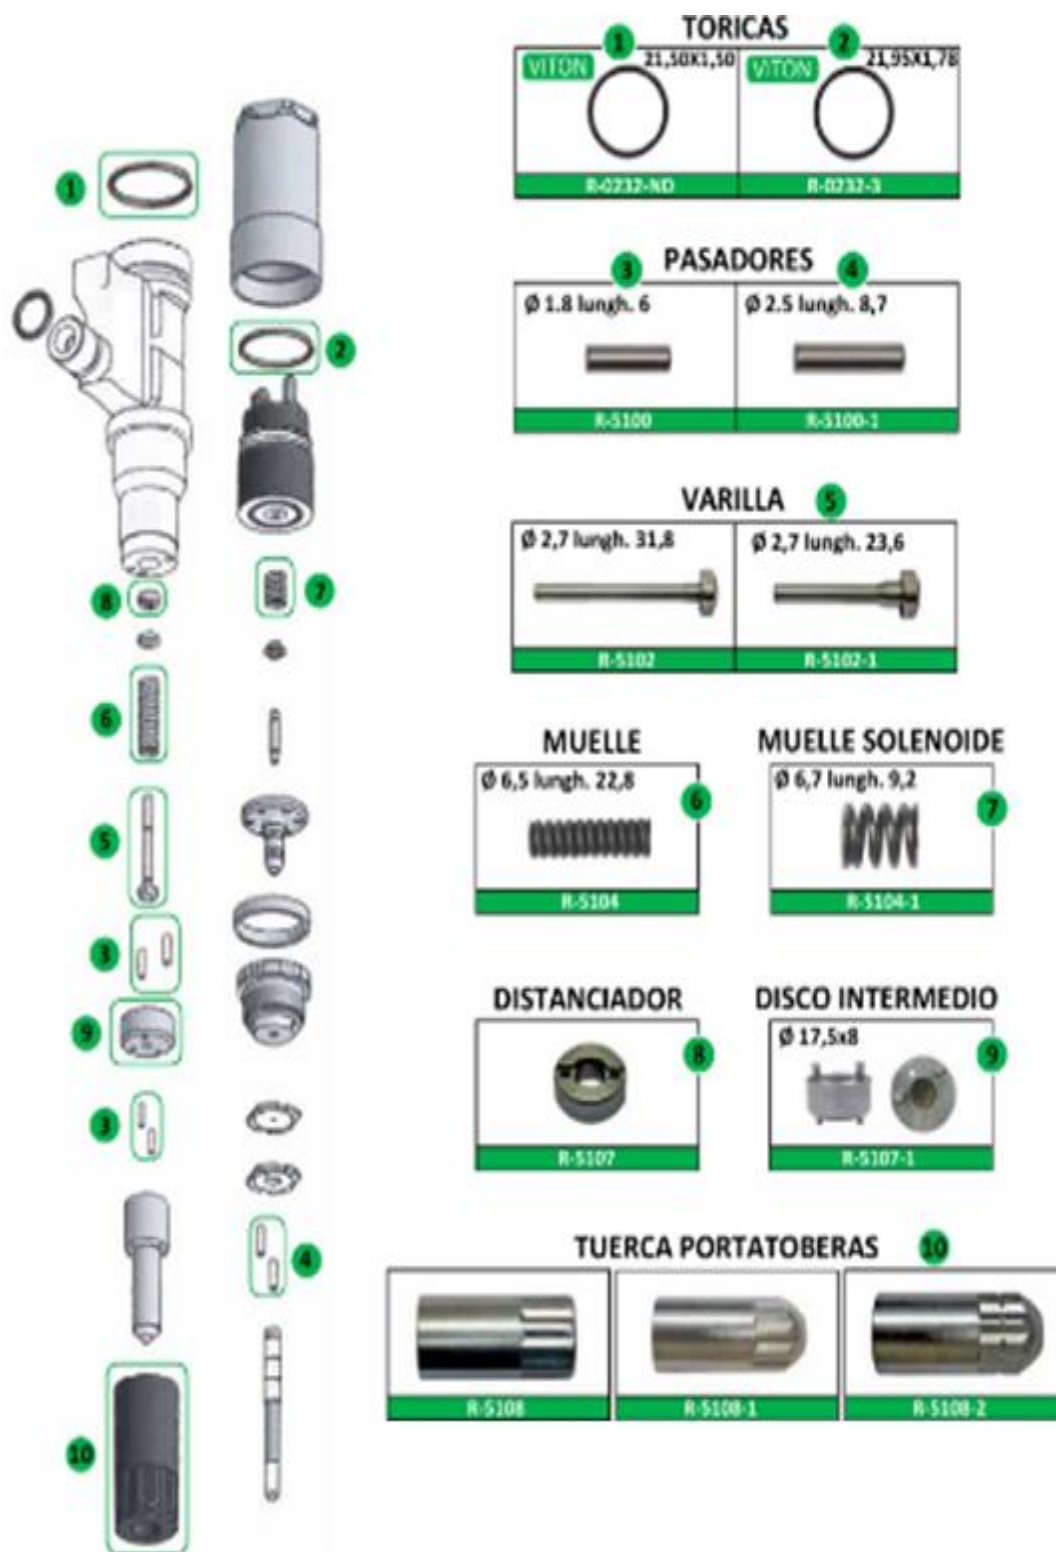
Despiece del inyector CRDI DENSO "06S000387"
